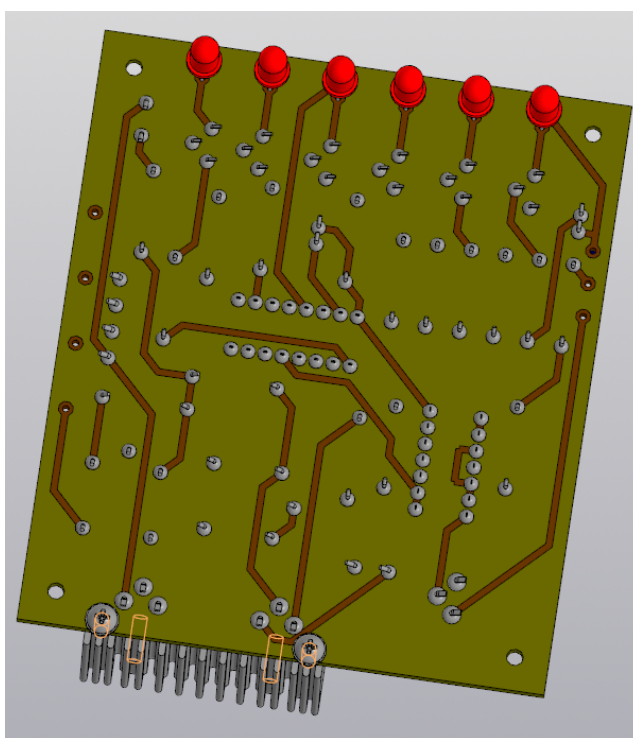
D вигляд плати друкованої з сторони пайки
